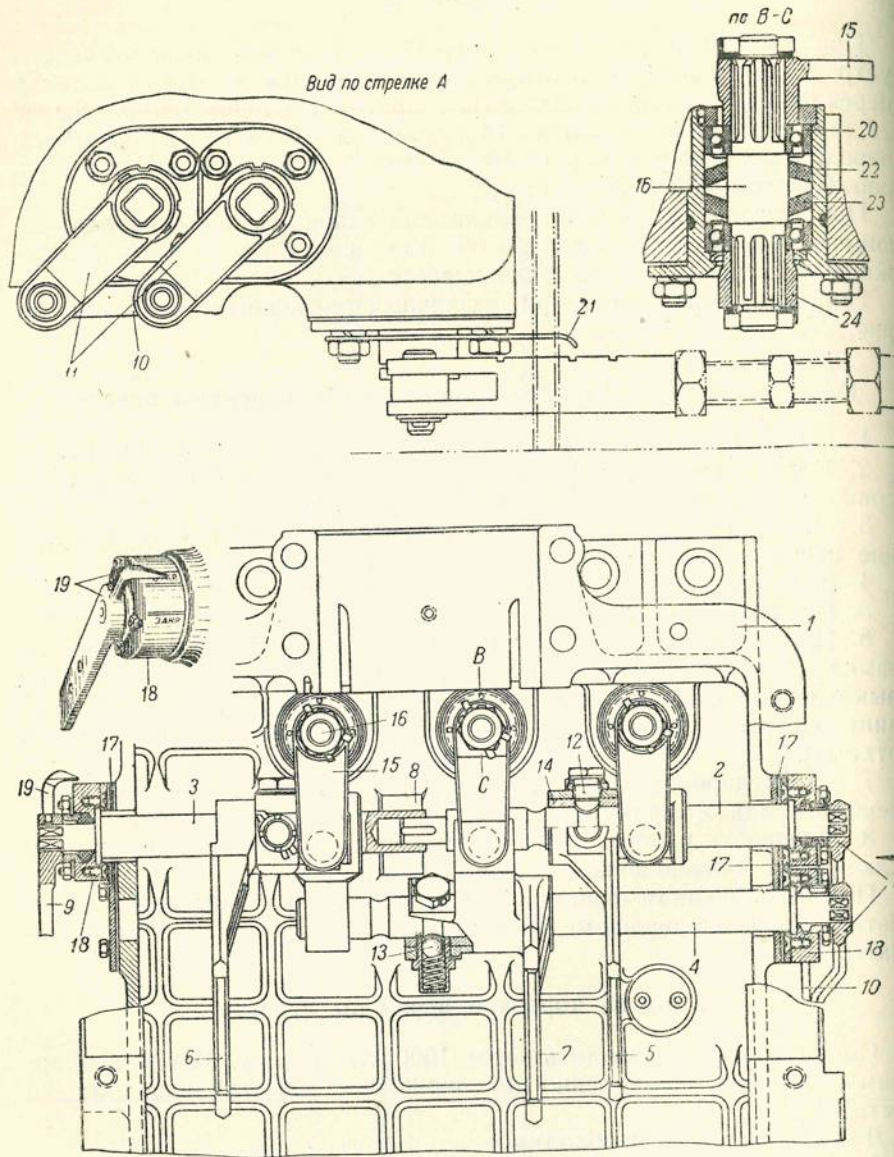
Переключающее устройство коробки перемены передач и замковый механизм:
